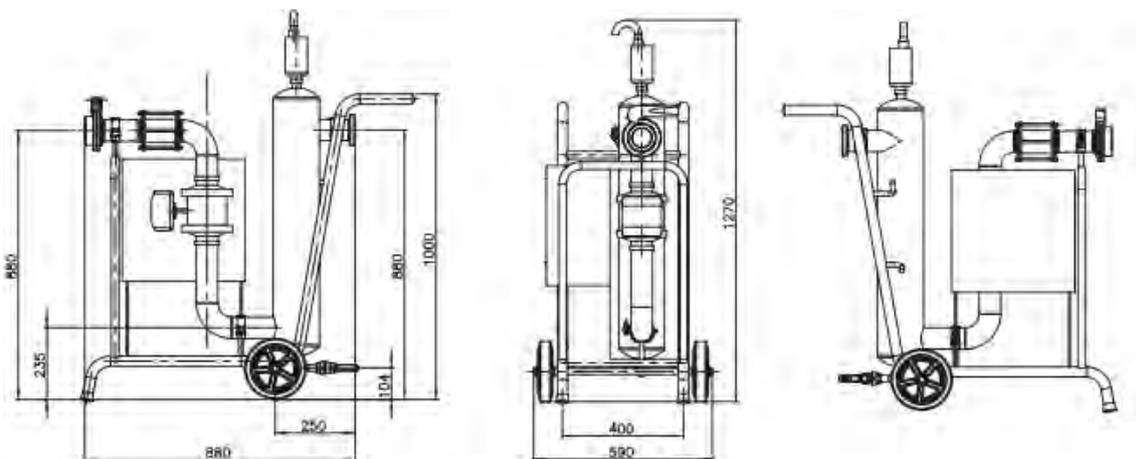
Dimensionado del equipo caudalímetro desaireador.
